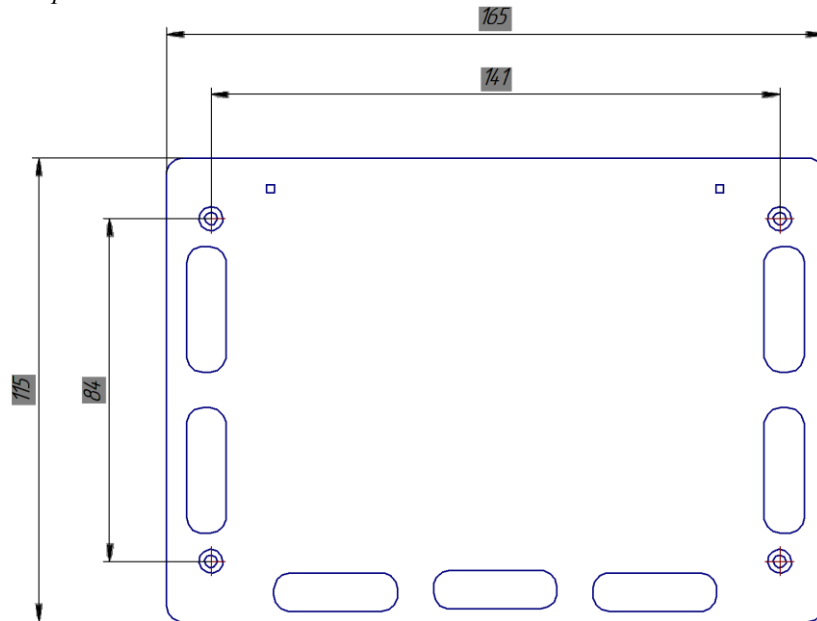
Разметка крепления АПИ в пластмассовом корпусе.
